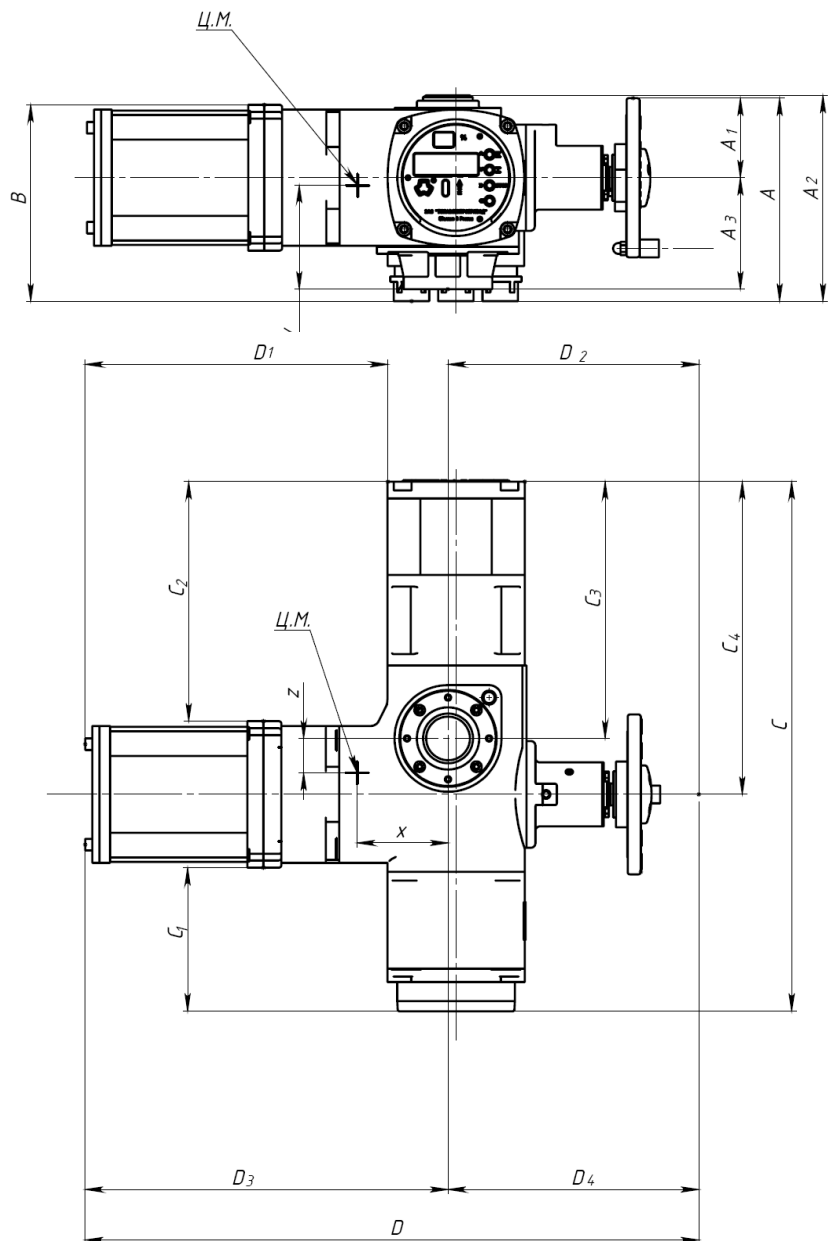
а – Габаритные размеры привода конструктивной схемы 41
